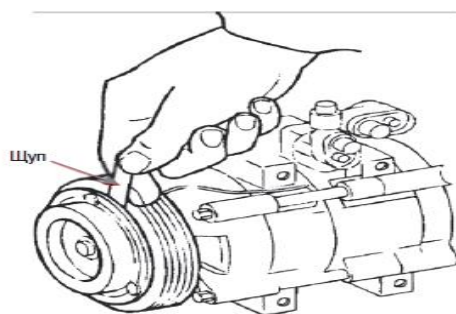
Практическая проверка зазора сцепления компрессора кондиционера
